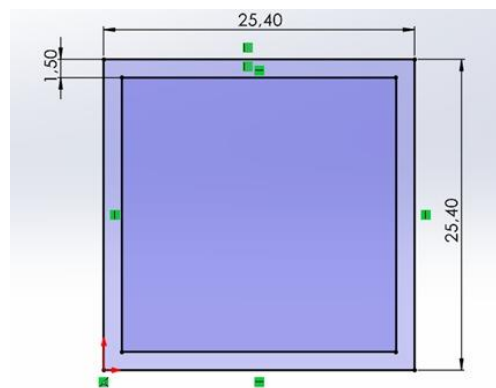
Estructura de acero del lisímetro en SolidWorks.
